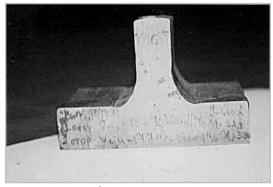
Макрошлиф сварного соединения выполненного «в лодочку» под флюсом проволокой \emptyset 4 мм
